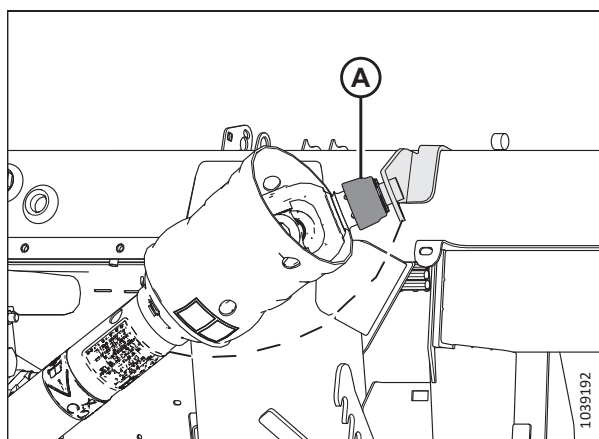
Приводний вал у положенні для зберігання — приводний вал Sidehill/Hillside B7180, B7181 або B7326
